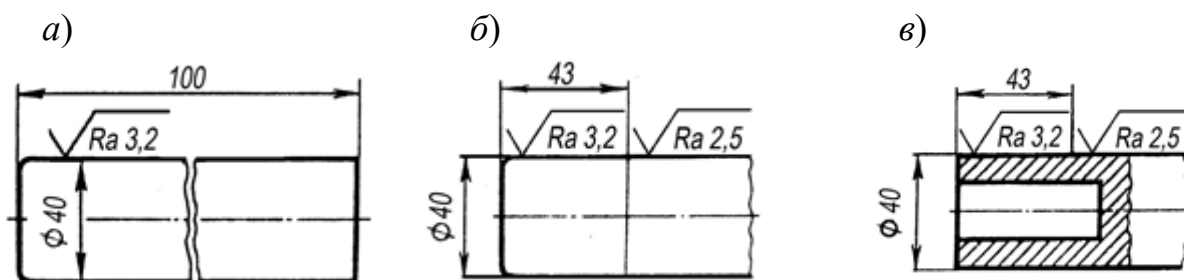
Расположение знаков шероховатости на изображениях чертежа
